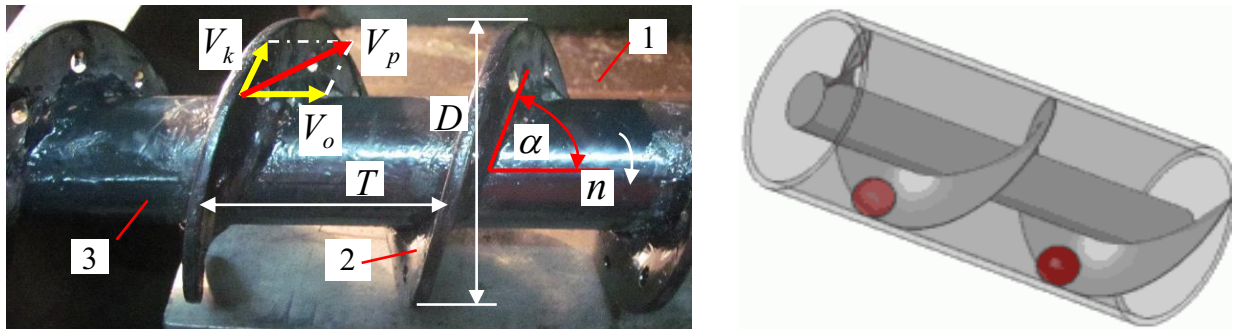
Загальний вигляд гвинтового конвеєра: 1 – кожух; 2 – виток шнека; 3 – барабан
